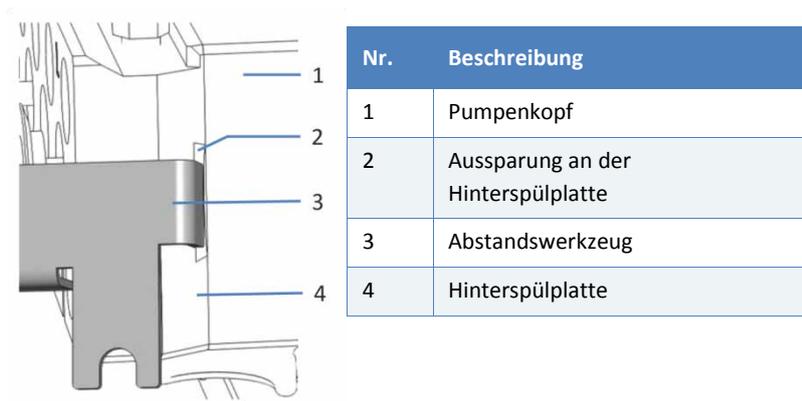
Entfernen der Hinterspülplatte mit dem Abstandswerkzeug
